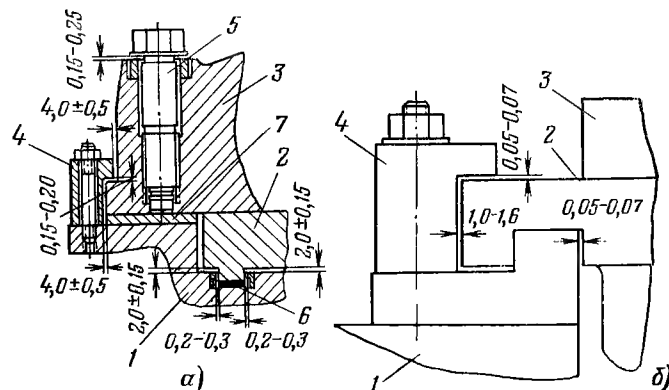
Соединение консольных лап ЦВД с корпусом переднего подшипника.
